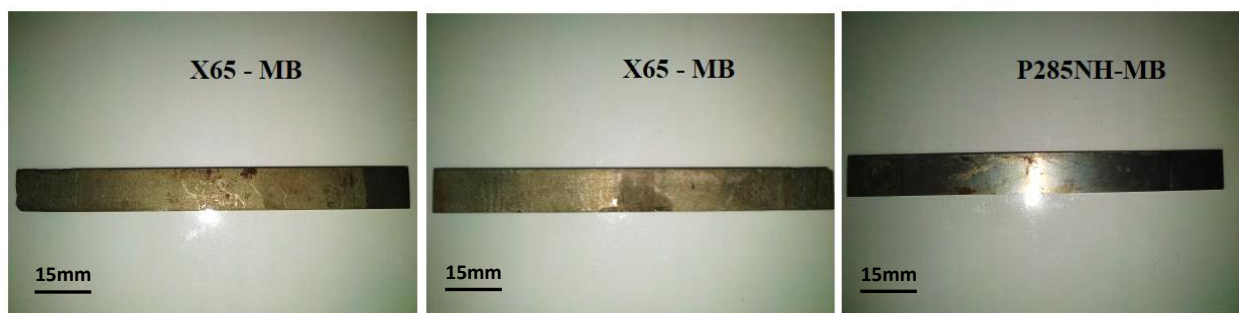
Eprouvettes de F4P en milieu LDT à 90°C après décapage
